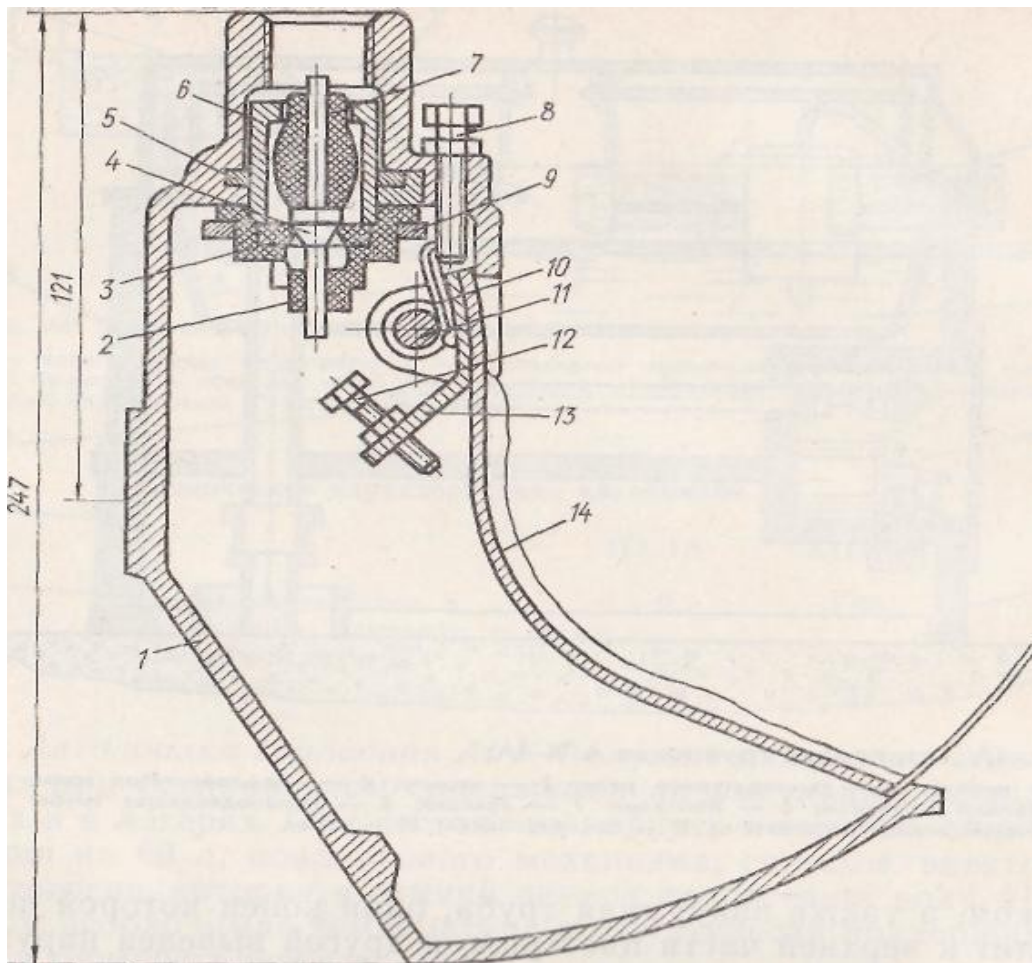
Автонапувалка ПСС- 1, що самоочищається : 1 - напувальна чаша; 2 - кришка клапана; 3 - сідло клапана; 4 - клапан- 5 - прокладка ущільнювач; 6 - склянка; 7 - амортизатор; 8 - регулювальний болт нажимного важеля; 9 - планка притискна; 10 - пружина; 11 - вісь кришки напувальної чаші; 12 - регулювальний
